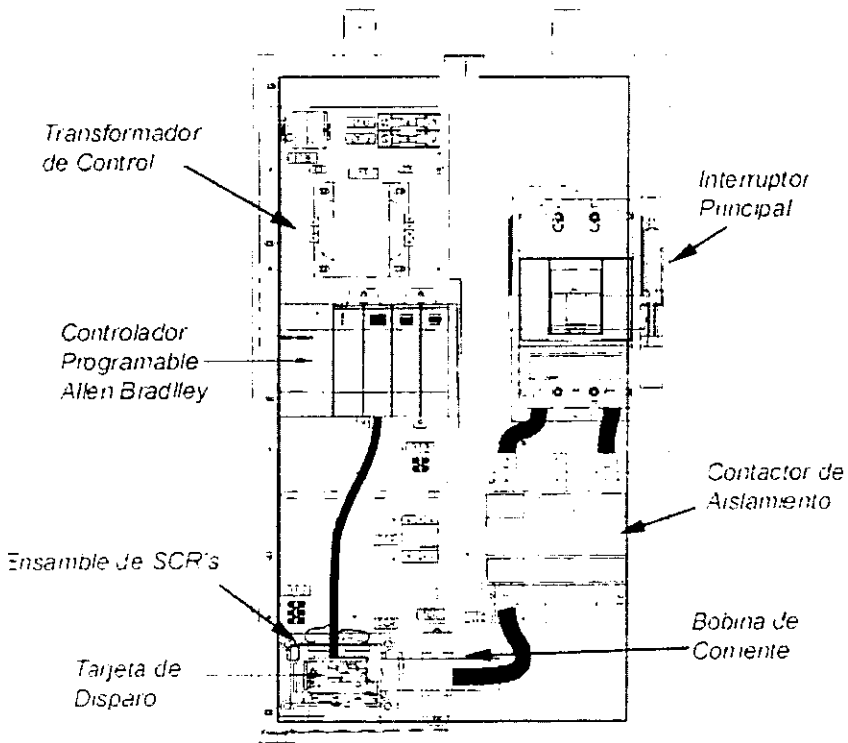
Control de soldadura Medar 3005.
